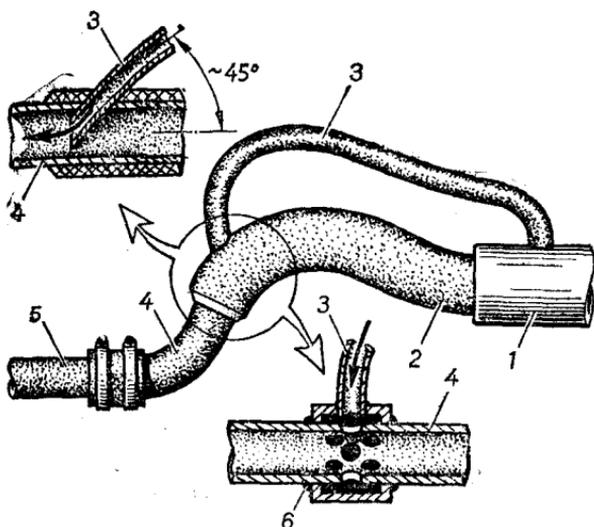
Крепление выхлопной трубы с помощью дюритового соединения.
